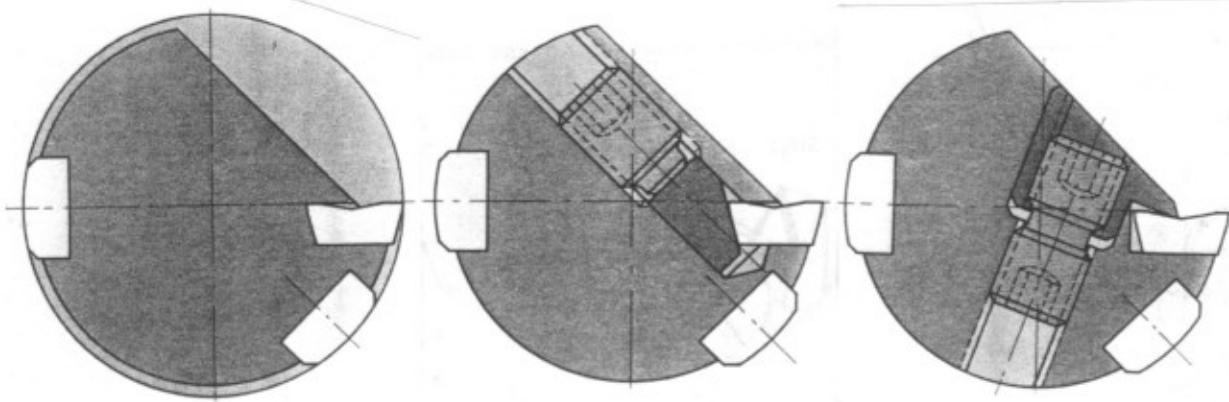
Příklady konstrukce tvarových prismatických soustružnických nožů používaných ve velkoseriových výrobách. Řezná část nástroje je výmenná, upnutá upínkou nebo šroubkem.
